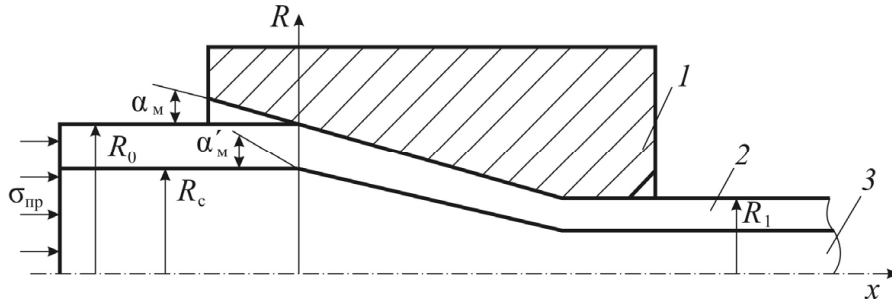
Схема прессования биметаллической сборной заготовки:
